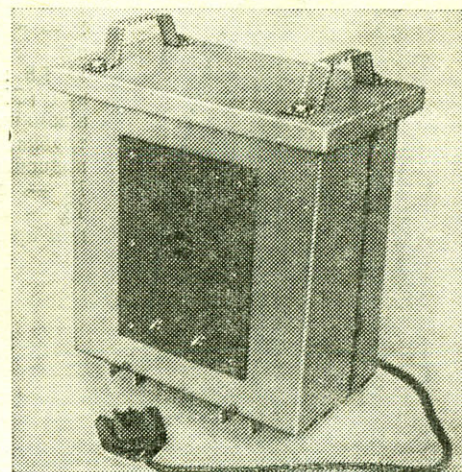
Сварочный трансформатор: 1 — корпус, 2 — крышка вентиляционного окна, 3 — крышка корпуса, 4 — ручка, 5 — гнездо, 6 — вилка, 7 — клемма, 8 — болт для подключения заземления.
